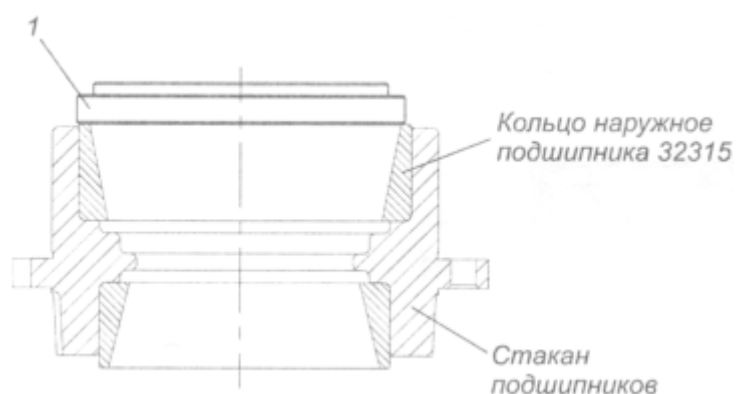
Запрессовка наружного кольца подшипника 32315В Р6: 1 - Оправка МАД804.40.243
